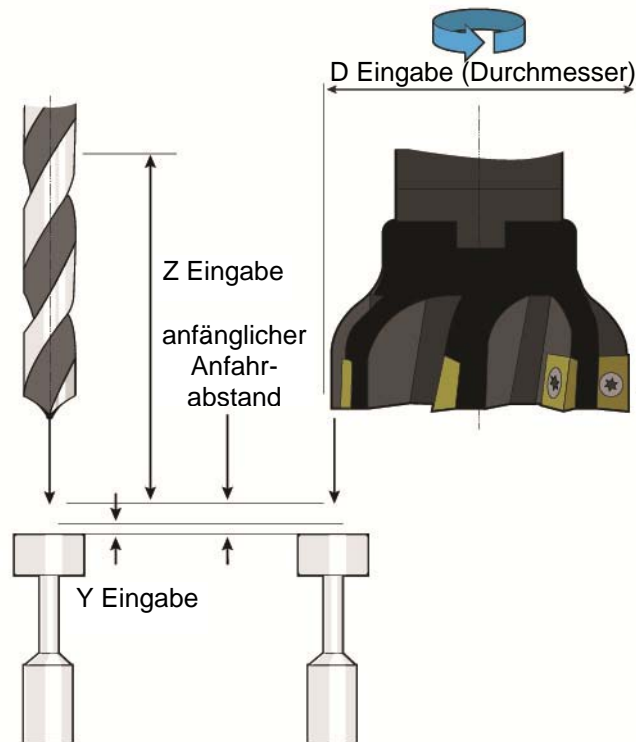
Überprüfung auf Werkzeugbruch bei rotierendem Werkzeug
